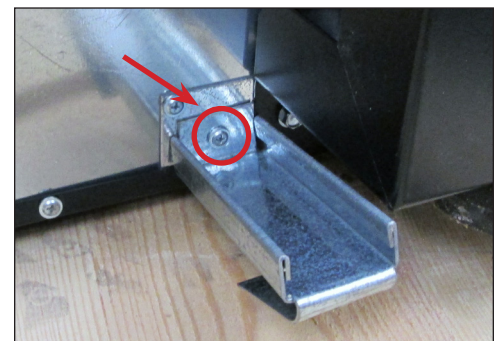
Entfernen Sie alle Befestigungsbügel vom Gerät durch Lösen der Schrauben (roter Kreis). Der Pfeil zeigt auf das hintere Metallplättchen.
